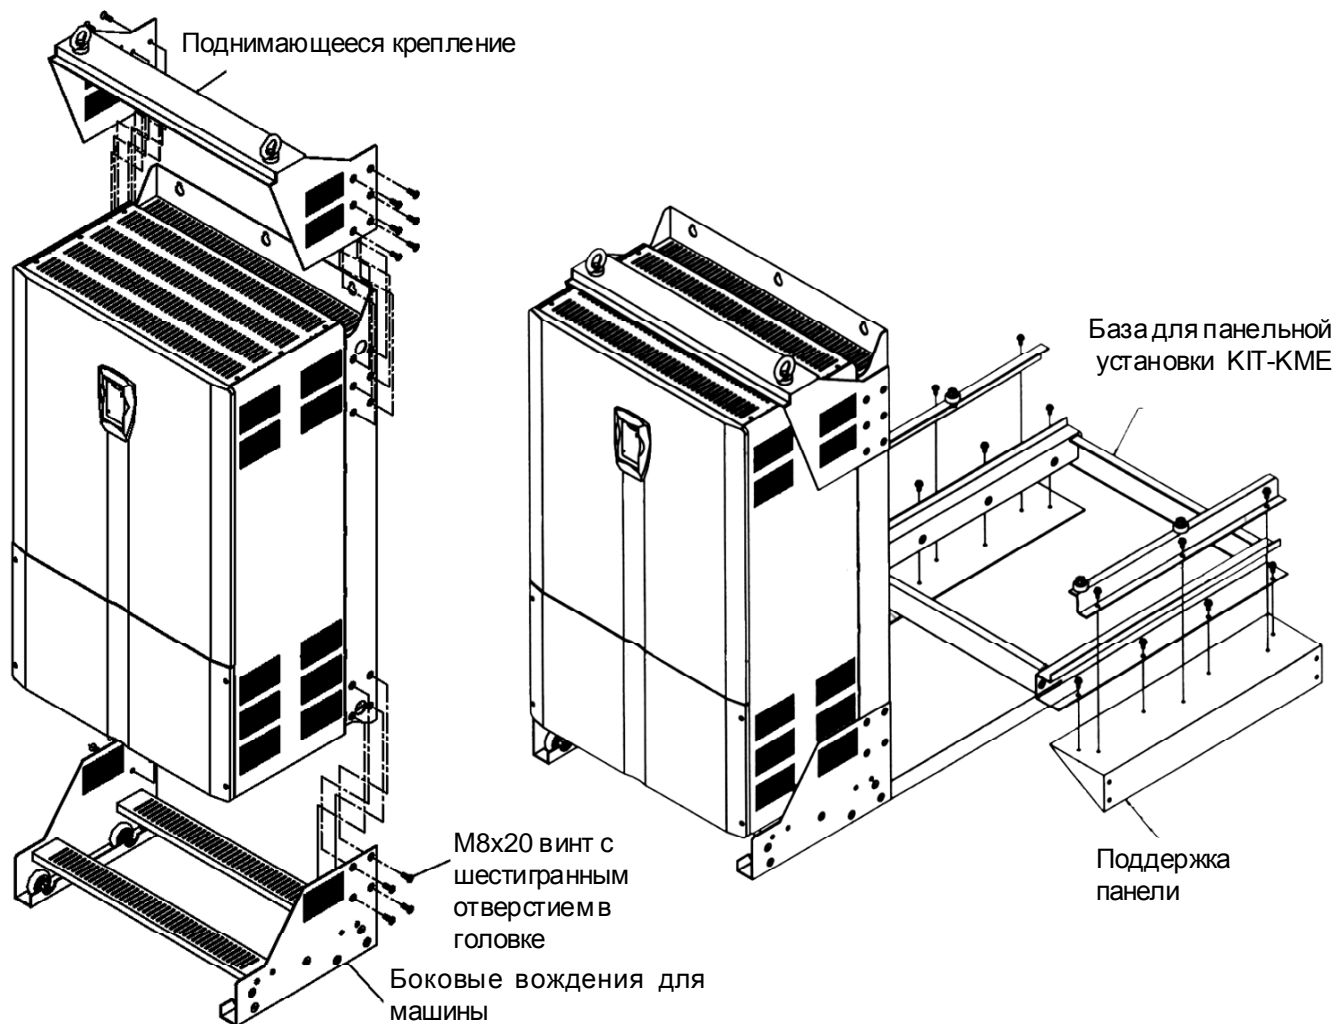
Установка КИТ-КМЕ на инвертор
